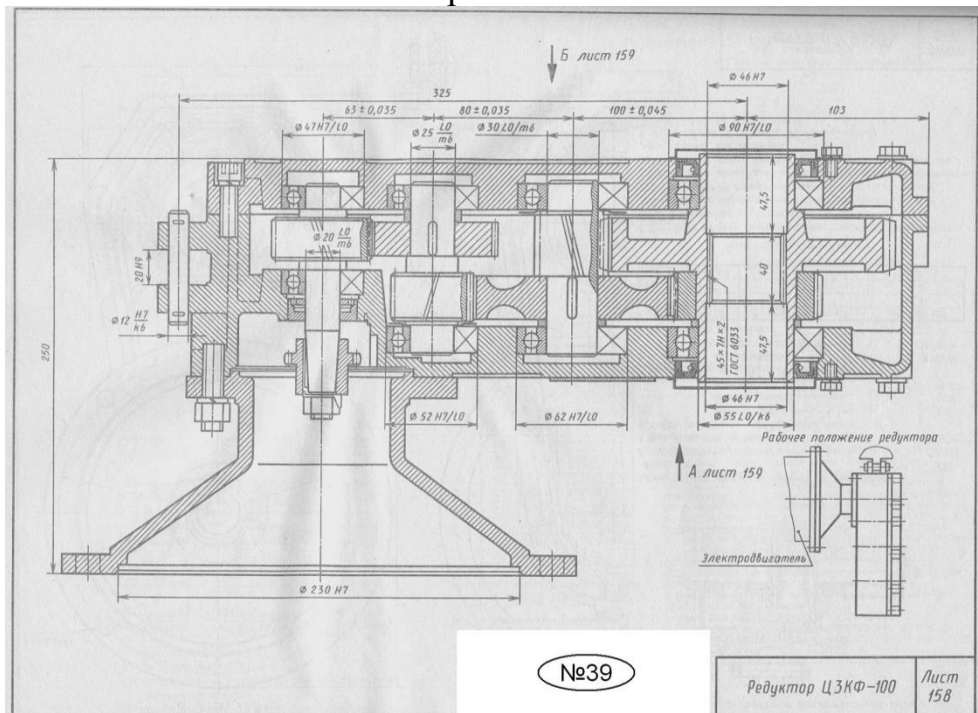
Цилиндрический двухступенчатый соосный редуктор
